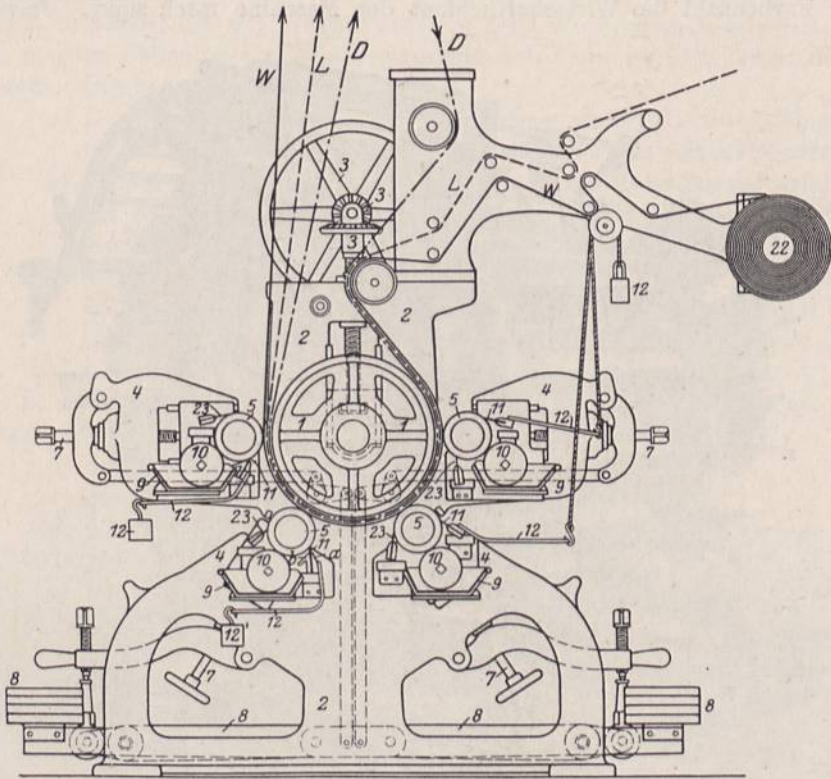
Schema einer Vierfarbenrouleaudruckmaschine.
